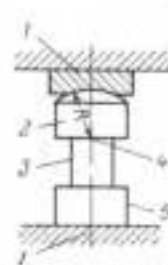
Шаровые опоры для испытания на сжатие: 1 — плита машины; 2 — опоры с шаровой поверхностью; 3 — образец; 4 — центр шаровой поверхности и 5 — опорная подушка
